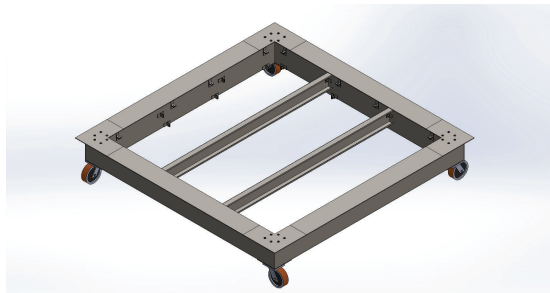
Estructura del piso del banco de pruebas (Fuente propia)
